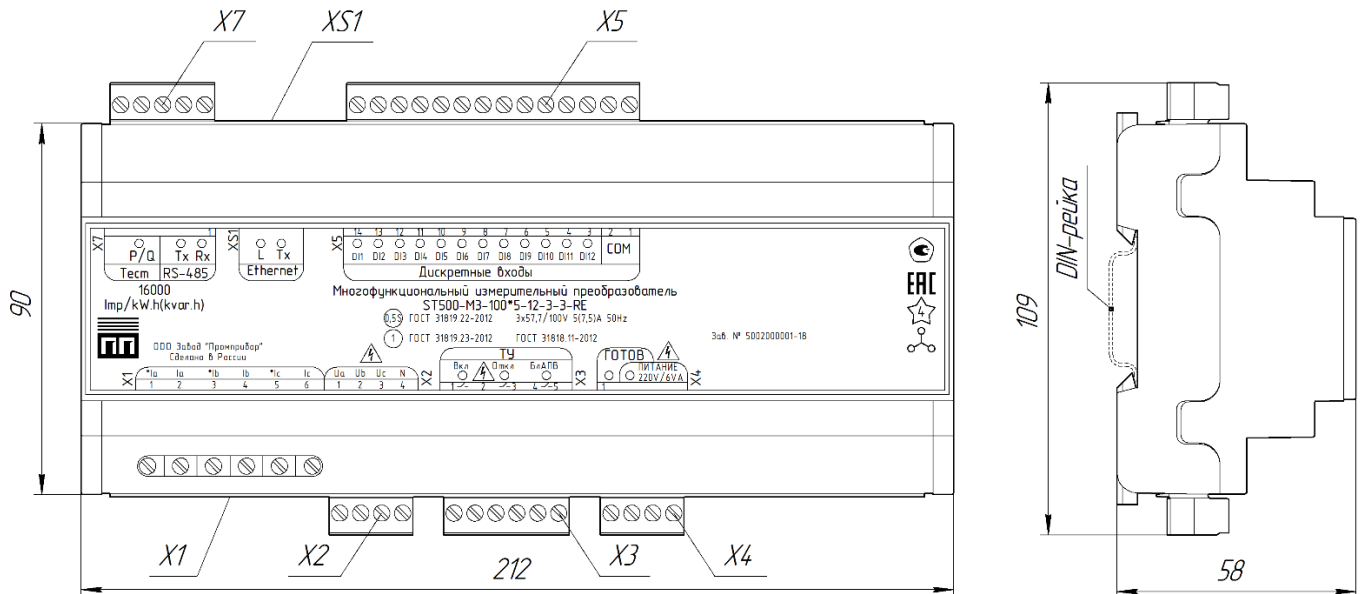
Внешний вид и габаритные размеры МИП
